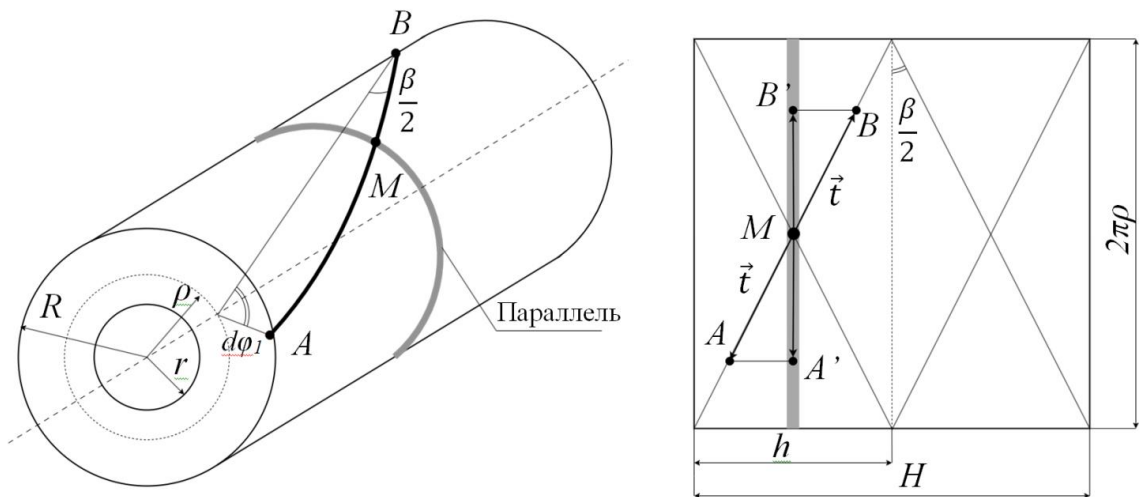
Схема крестовой намотки нити на паковку и ее развертка.
